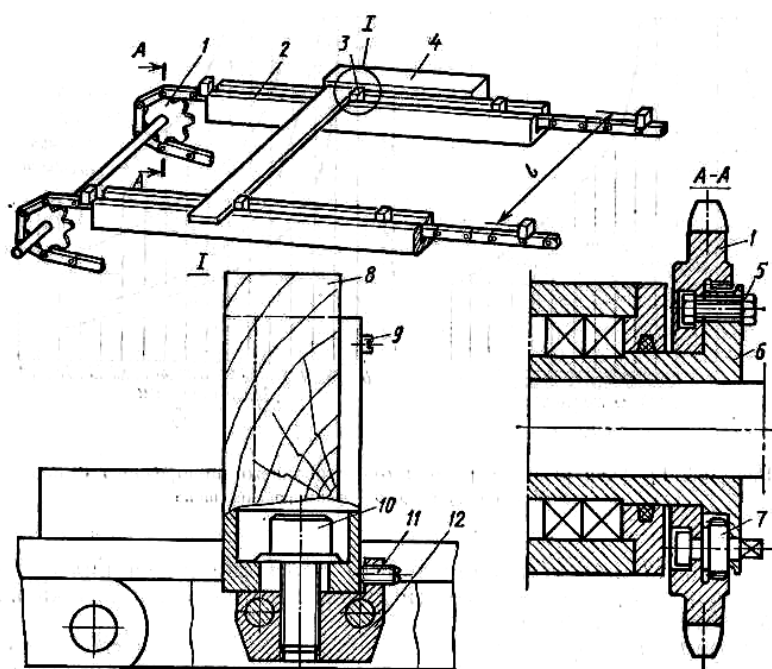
Наладка упоров конвейерной цепи шипорезного станка для рамных шипов:
